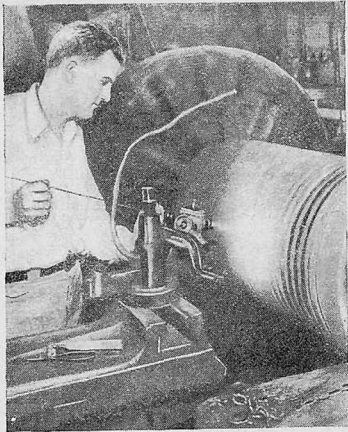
При ремонте цилиндрической детали ее закрепляют на токарном станке, а «пистолет» устанавливают на суппорте станка
